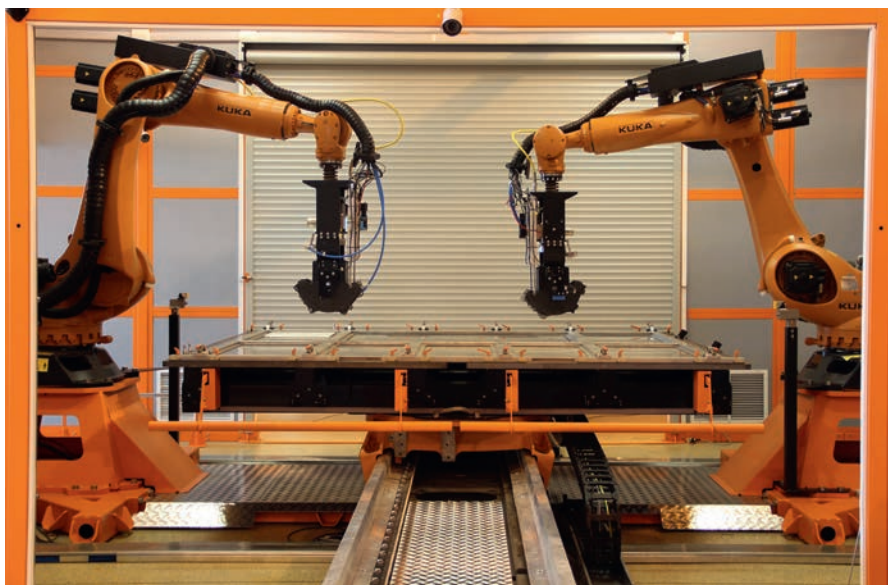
Роботизированная установка лазерной сварки боковин вагонов метро. Фото: «НТО «ИРЭ-Полюс»
